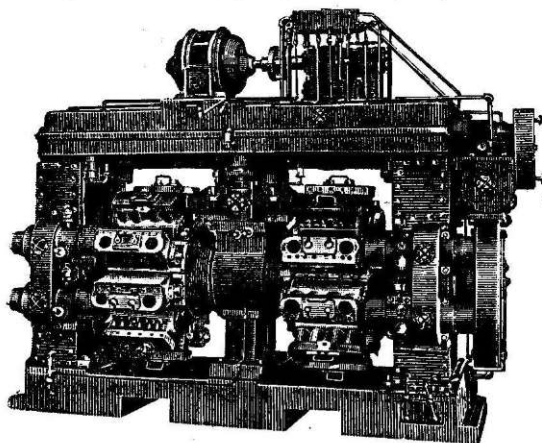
Четырехшпиндельный фрезерный станок барабанного типа.
